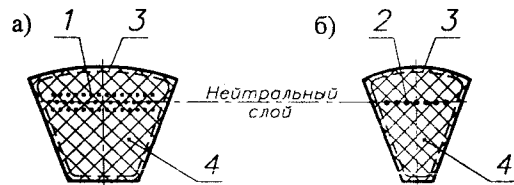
Конструкции клиновых ремней: а) кордтканевая (ремни нормальные); б) кордшнуровая (ремни узкие); 1 - кордткань; 2 - кордшнур; 3 - обкладка; 4 - наполнитель (резина)
